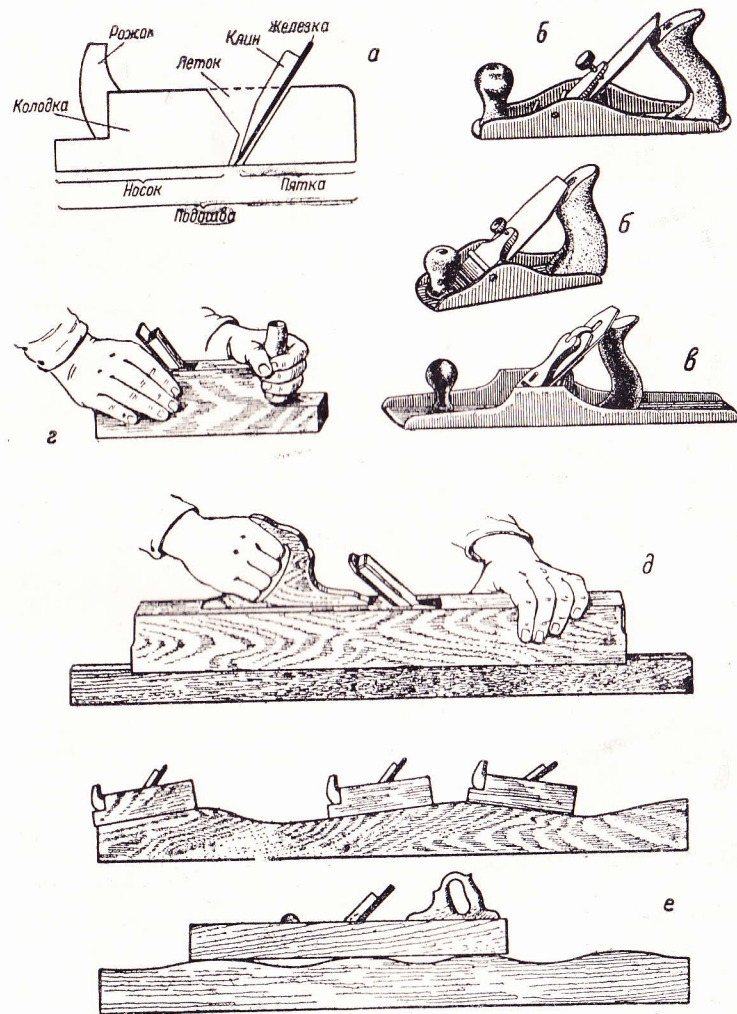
Рубанки: а — схема рубанка; б — металлические рубанки; в — металлический фуганок; г — как держать рубанок; д — как держать фуганок; е — строжка длинной доски рубанком и фуганком.
